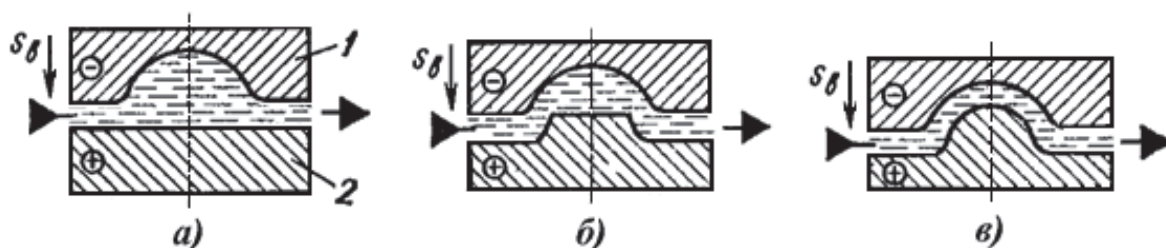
Схема послідовного (а, б, в) формоутворення поверхні заготовок: 1 – електрод-інструмент; 2 – електрод-заготовка
